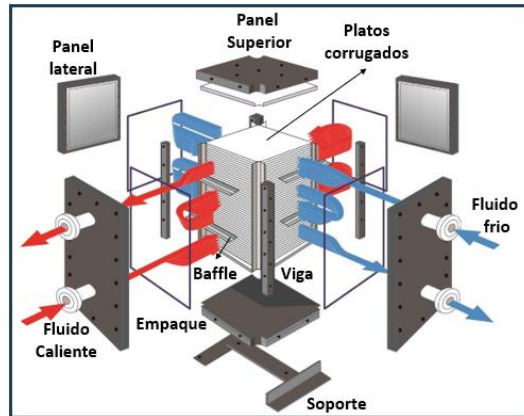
Intercambiador de calor de placa soldada tipo Compabloc.
